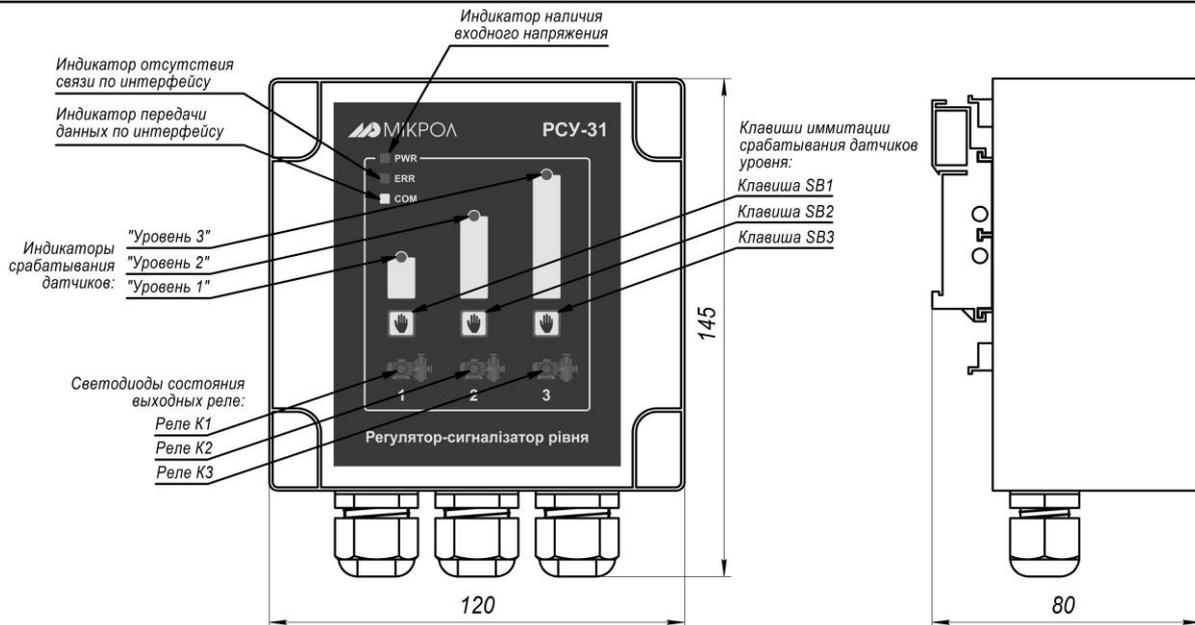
Внешний вид и габаритные размеры PCY-31
